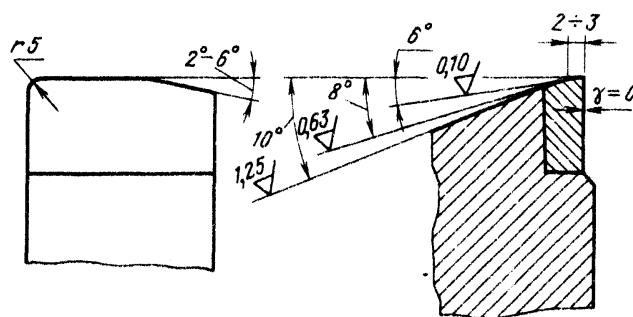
Стругальный резец для чистовой обработки плоскостей
